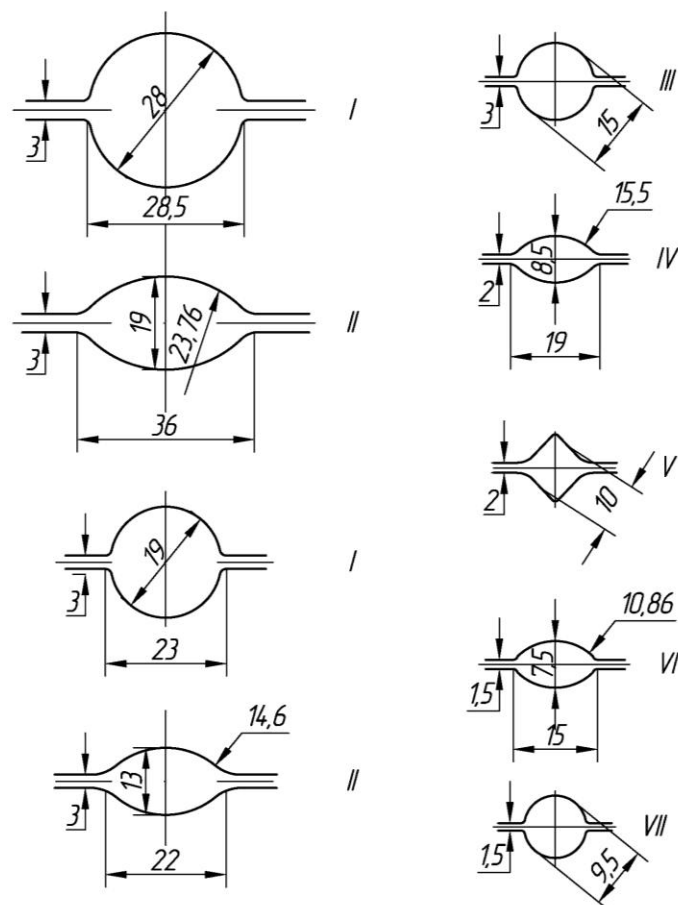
Калибровка чистой линии стана для прокатки биметаллической сталемедной катанки (I – VII – номера калибров)
